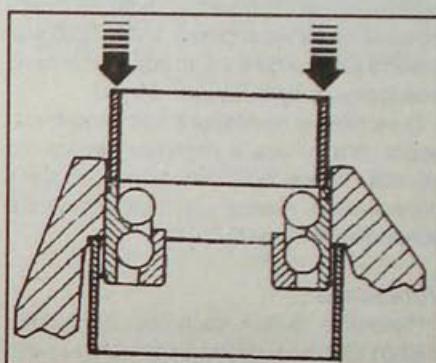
Использование прессы и оправок Rou. 1392 и Т. Ав. 1230 для выдавливания наружного кольца подшипника из поворотного кулака
